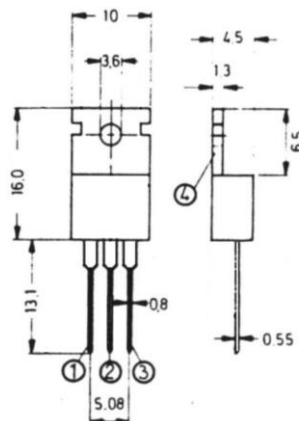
Габаритні розміри стабілізатора LM7812
